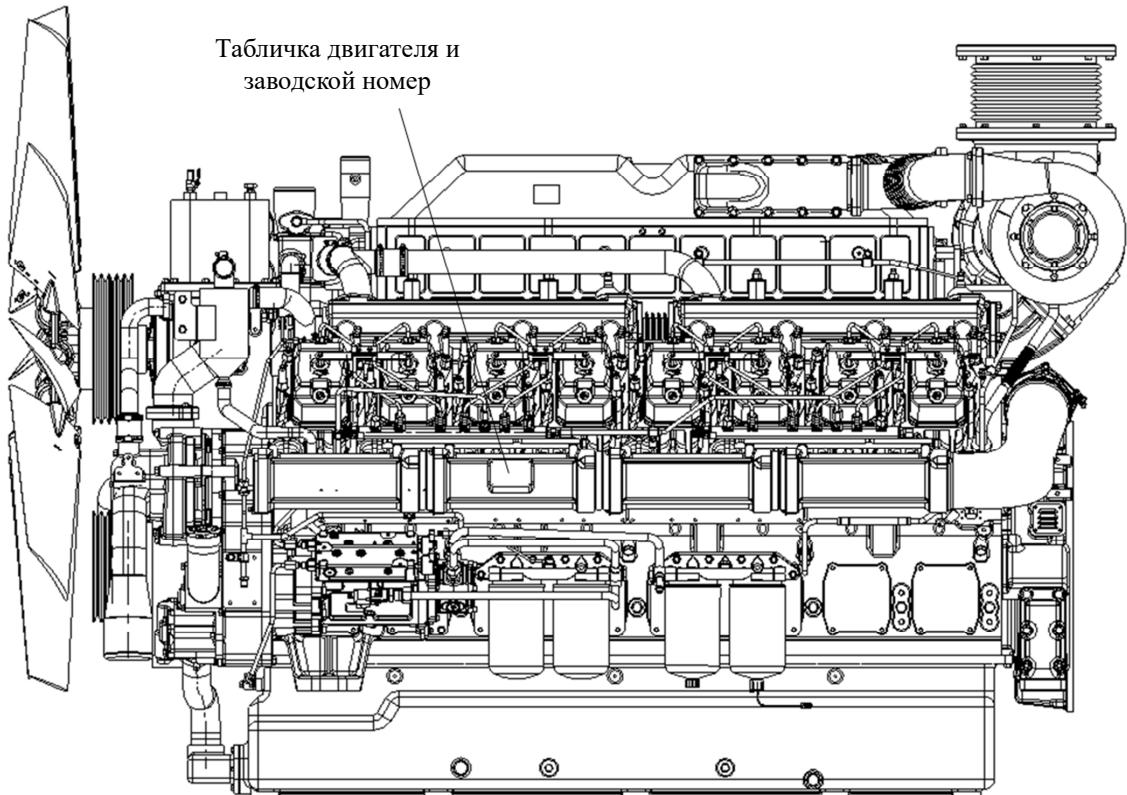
Маркировка двигателя и расположение заводского номера
